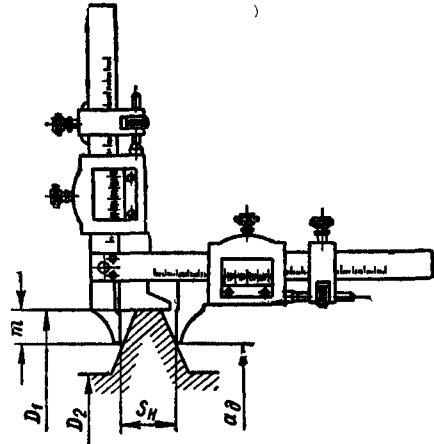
Измерение профиля зуба червяка с помощью зубомера.
